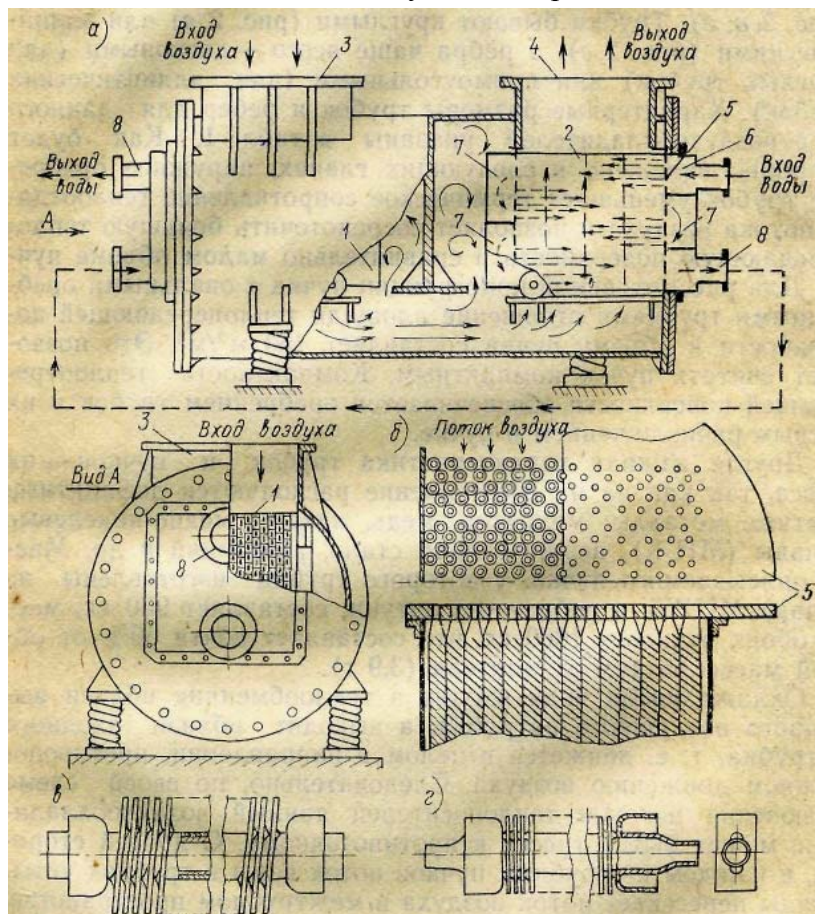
Устройство воздухоохлаждателя: а - общая схема; б - трубный пучок; в и г - оребренные трубки.
